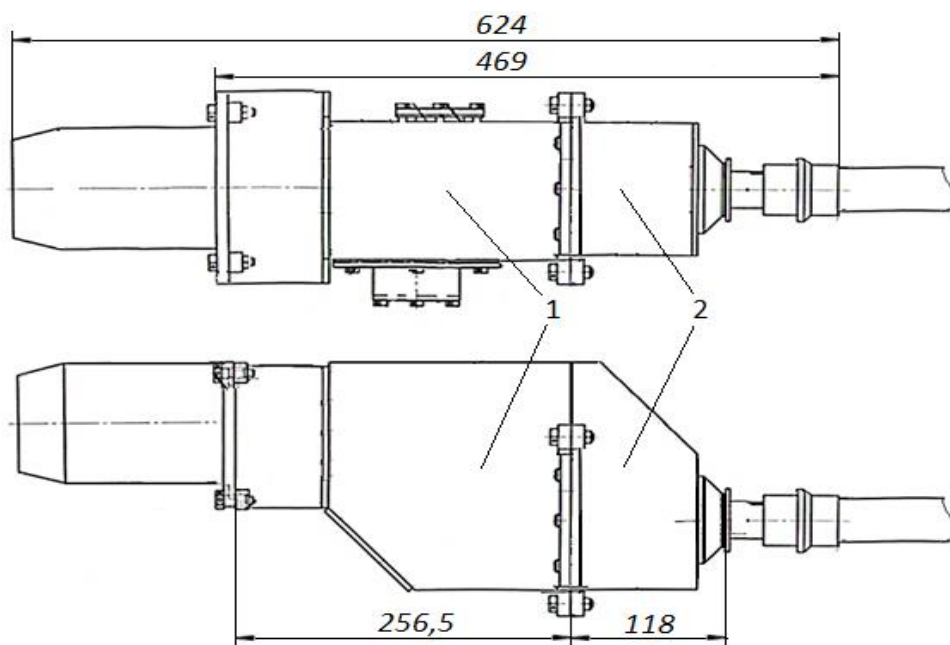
Принципиальная схема опытного образца ручного перфоратора
